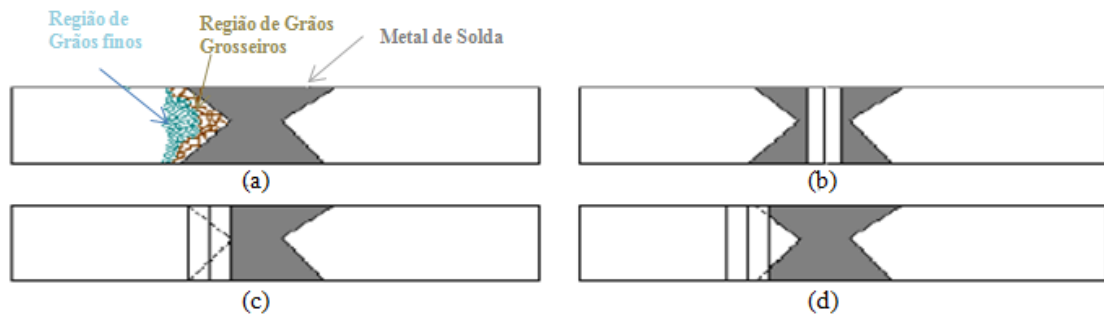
(a) Ilustração esquemática das regiões da junta soldada; (b) vista superior do entalhe no centro do metal de solda; (c) vista superior do entalhe na região de grãos grosseiros da ZTA; (d) vista superior do entalhe na região de grãos finos na ZTA (ALBUQUERQUE, 2009).
